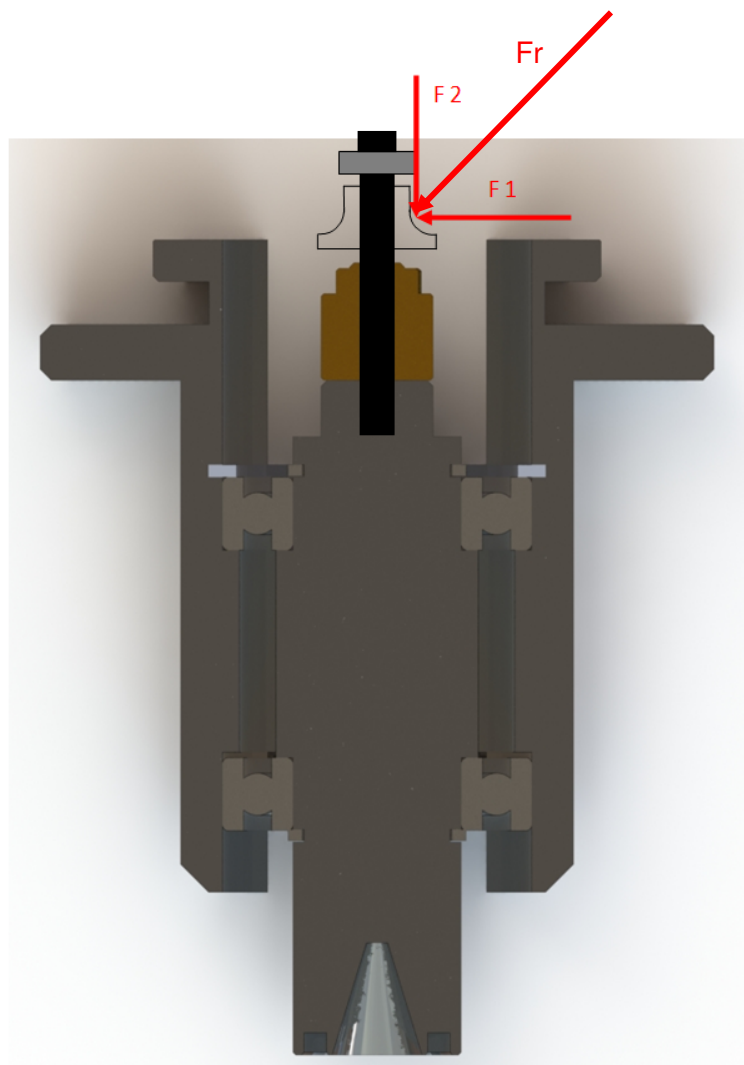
Werkzeughalter 1 Schnittansicht 2
